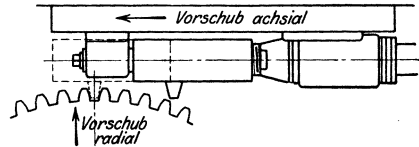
Fräsen eines Schneckenrades mit Schlagzahn.
